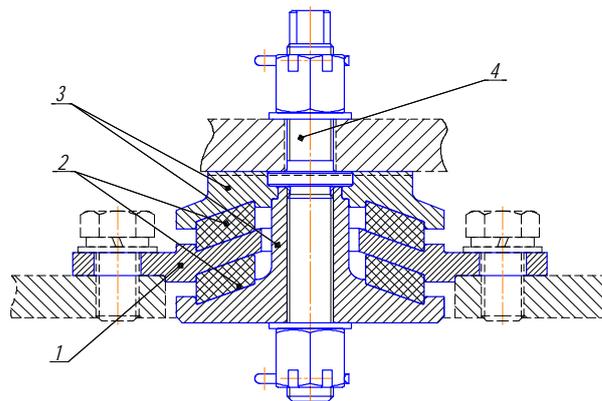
Конструктивная схема виброизолятора ВВК-01: 1-корпус, 2 – УДЭ, 3 – шайбы, 4 – винт
